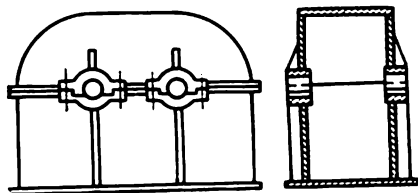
Corps soudé d'un démultiplicateur
